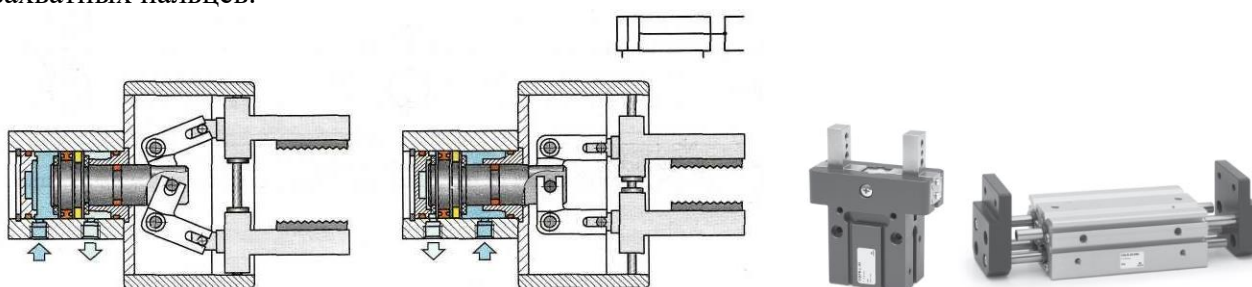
Пневматический захват с параллельным движением пальцев
